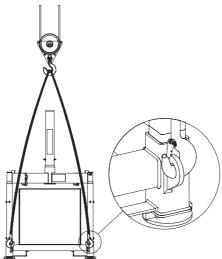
Подъем установки в сборе для перемещения (при использовании крана).
